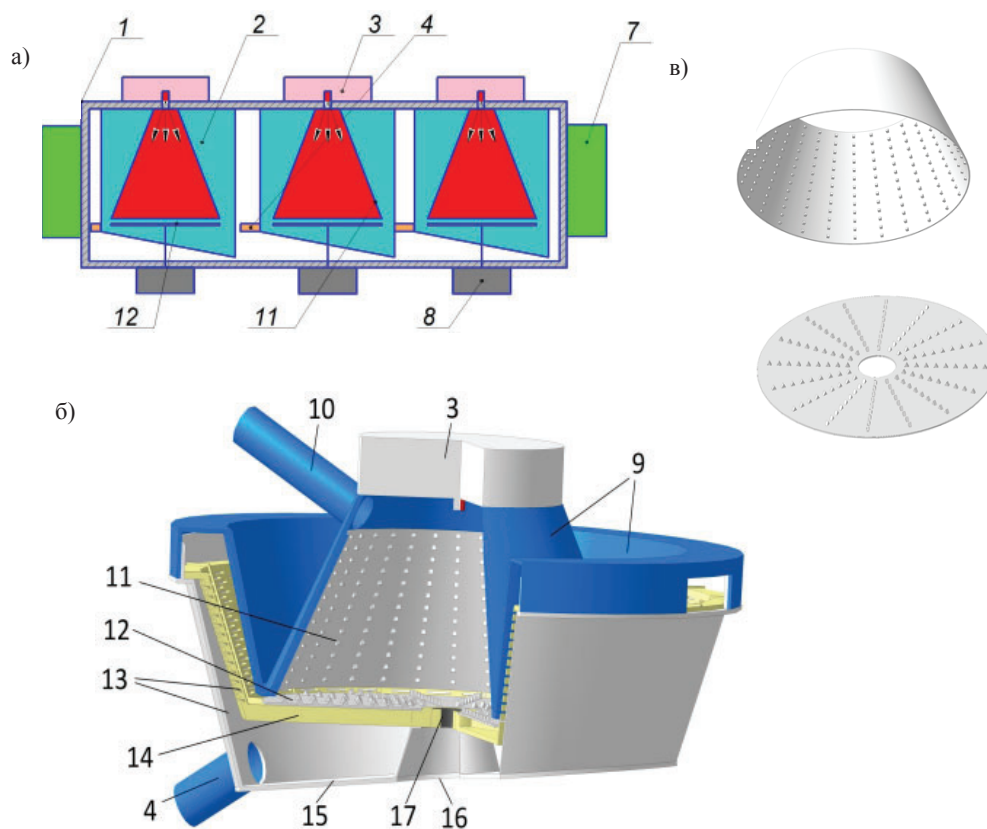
Многомодульная центробежная сверхвысокочастотная установка для термообработки сырья и отделения жидкой фракции: а) схематическое изображение; б) рабочая камера в разрезе; в) конический резонатор из двух частей; 1– цилиндрический экранирующий корпус; 2 – рабочие камеры; 3 – сверхвысокочастотные генераторные блоки; 4 – сливные патрубки; 5 – ёмкость для жидкой фракции; 6 – измельчители «Волчок»; 7 – ёмкости для твёрдой фракции; 8 – электродвигатели; 9 – верхняя часть рабочей камеры; 10 – измельчающий механизм (нож и решётка, нагнетательный шнек); 11 – коническая часть резонатора (усечённый конус); 12 – дисковая часть резонатора; 13 – нижняя часть рабочей камеры; 14 – коническая тарелка из диэлектрического материала; 15 – поддон конический из ферромагнитного материала; 16 – отверстие для фиксатора тарелки и диска, выполненные в виде тёрки; 17 – отверстие для вала электродвигателя
